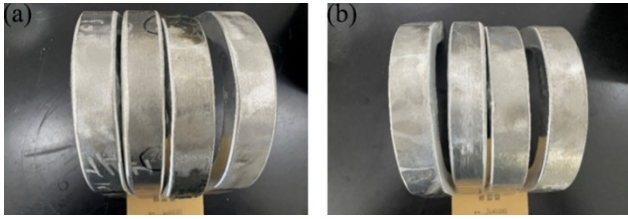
铝合金接头弯曲试验(a)MIG 焊接技术(b)TIG 焊接技术
